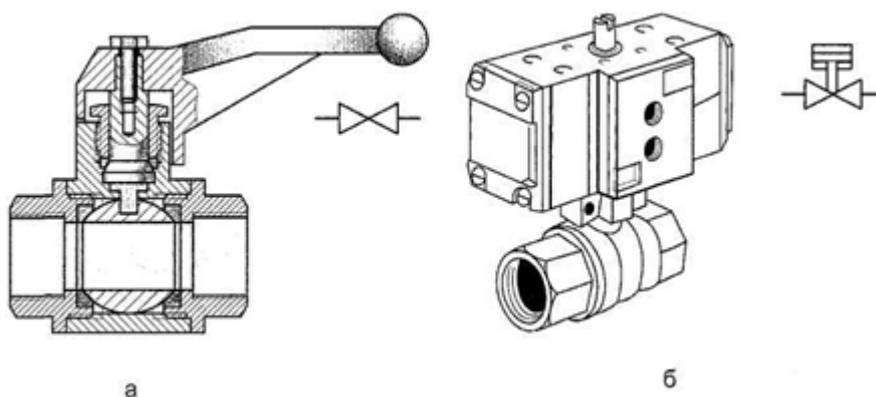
Шаровые вентили (конструкция и условное графическое обозначение на схемах): а) с ручным управлением; б) с пневматическим управлением
